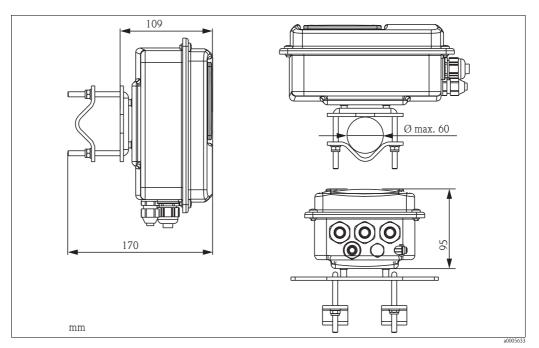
Montaje del CLD134 en tuberías Ø 60 mm
